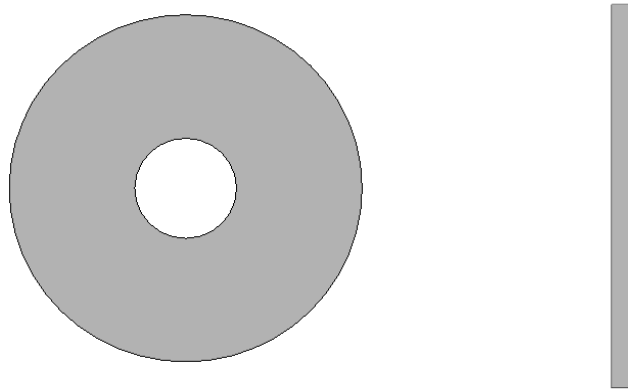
Vista en planta y perfil de las pesas de 5mm de espesor
